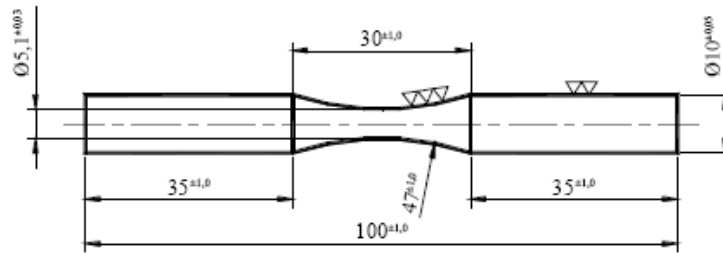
Dimensões do corpo de prova para o ensaio de fadiga.
